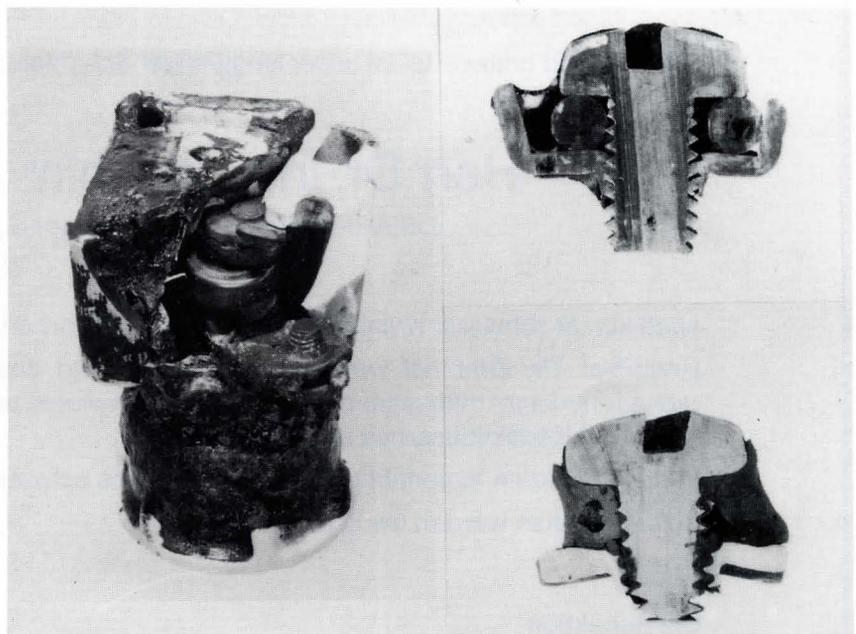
Sicherungselement mit Kabelanschlüssen (links); Schnitt durch Schraubenschluß: Vorschriftsmäßig mit Schraube befestigtes Kabel (rechts oben) bzw. verschweißte Zuleitung (rechts unten).
